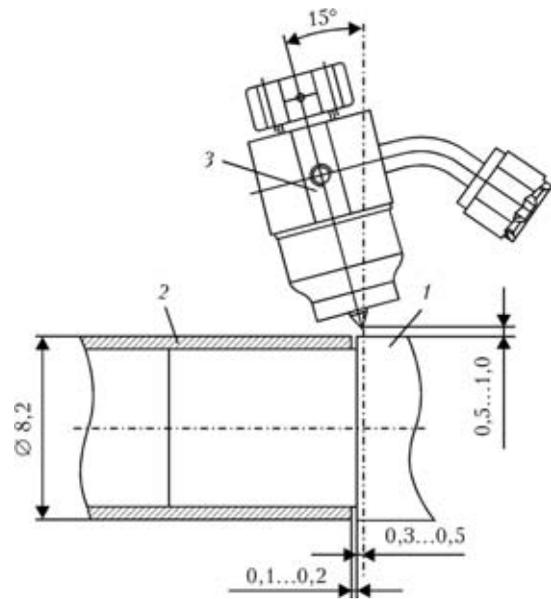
Схема собранного под сварку стыкозамкового соединения ПЭЛа: 1 — конус (наконечник); 2 — оболочка; 3 — горелка с неплавящимся электродом
